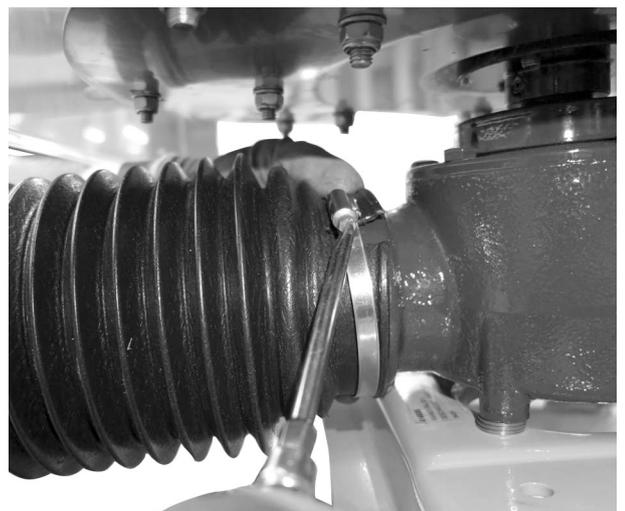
Gelenkwelle auf Getriebezapfen aufstecken
